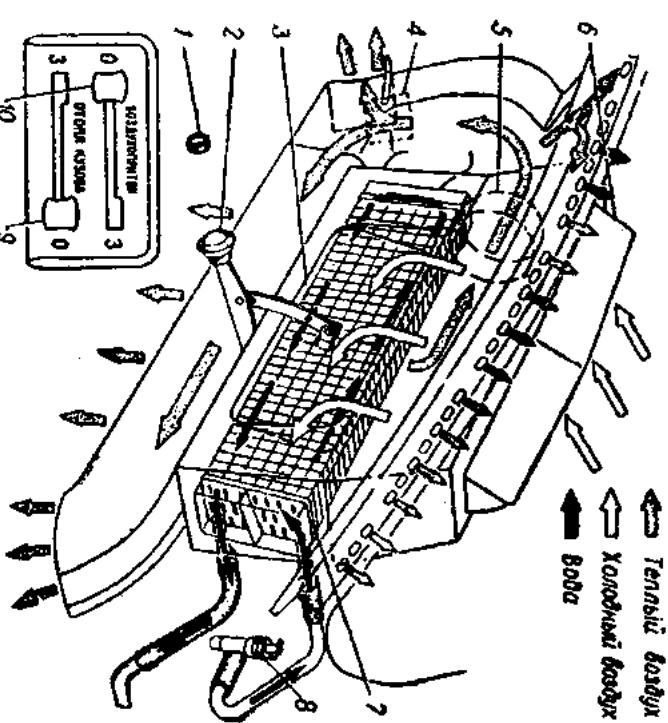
Устройство отопления и вентиляции кузова и оборудования ветрового стекла.
